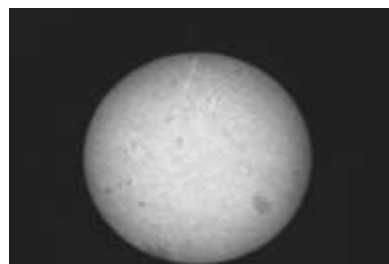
Поверхность заготовки из стали 45 после обработки (микроскоп МБС-9 (увеличение 40×))
